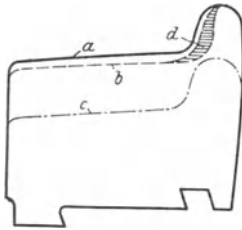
Aufschweißen abgelaufener Spurkränze.
